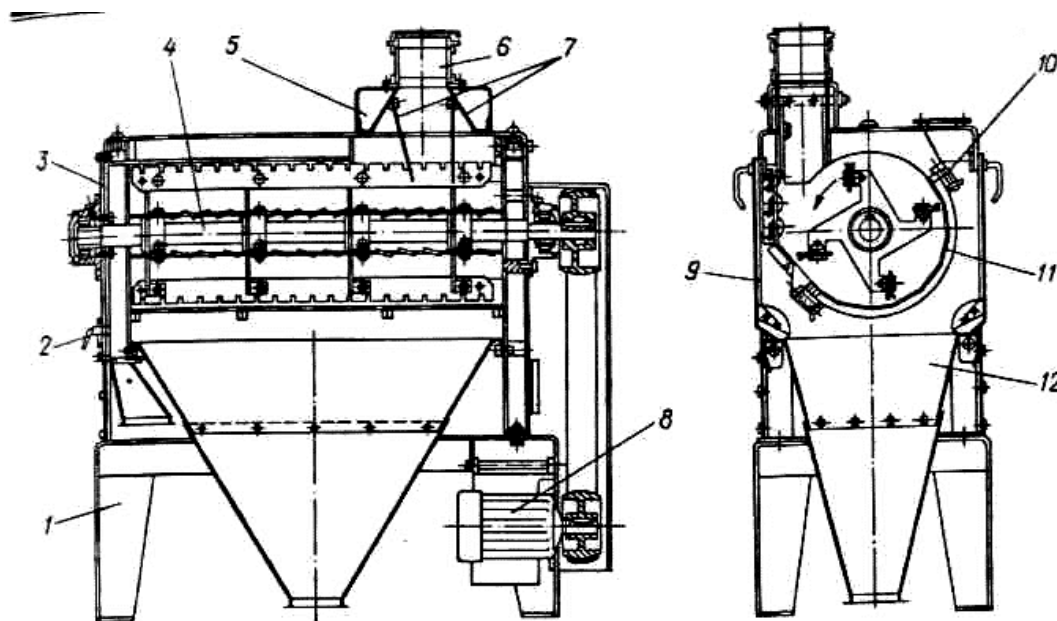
Вымольная машина А1-БВГ: 1 — подставка; 2 — люк; 3 — крышка станины; 4 — ротор; 5 — приемная камера; 6 — приемный патрубок; 7 — спаренные клапаны; 8 — привод; 9 — дверка; 10 — зажим; 11 — сито; 12 — конус
